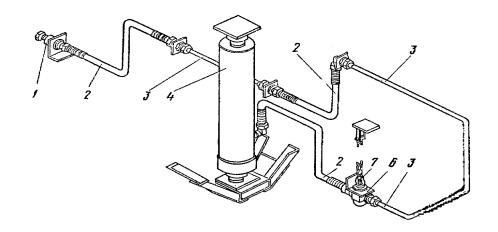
Схема соединений гидравлическая: 1 — муфта разрывная; 2 — шланг гибкий; 3 — трубка; 4 — гидроцилиндр; 6 — кран ограничения угла опрокидывания платформы; 7 — цепь; I — включен гидроцилиндр первого прицела;
